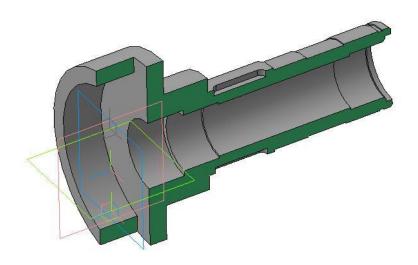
Твердотельная модель детали «Корпус фрикционной муфты»
